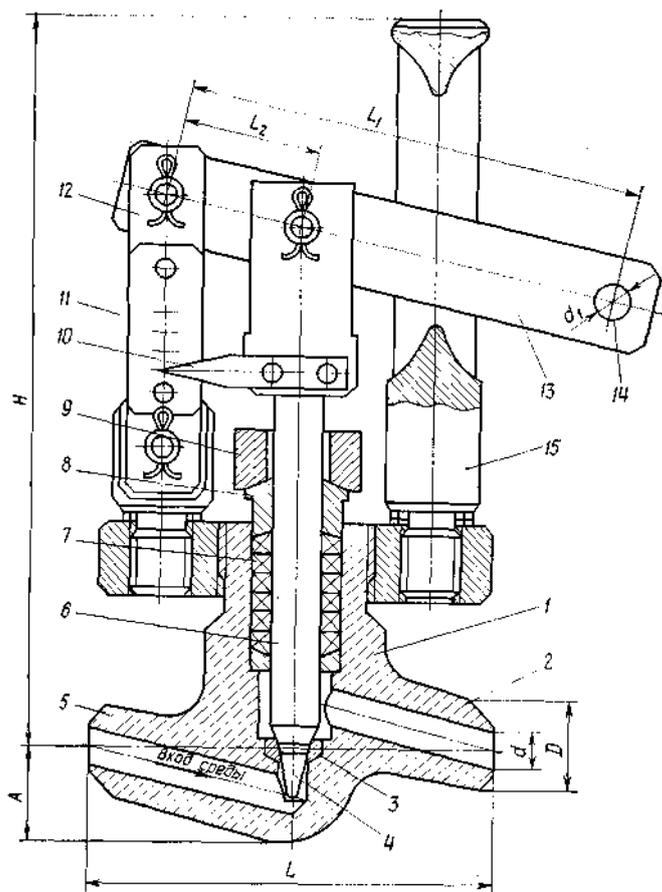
Клапан регулирующий игольчатый D_v 10, 20 серий 751, 1033
